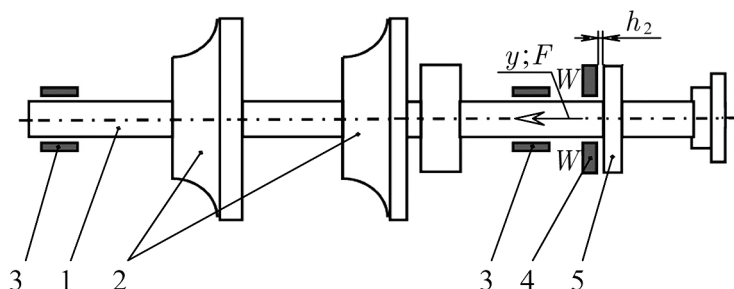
Схема роторной части центробежного компрессора: 1 – вал; 2 – рабочая ступень; 3, 4 – опорный и упорный подшипники скольжения; 5 – упорный диск;  $h_2$  – рабочий зазор упорного подшипника
